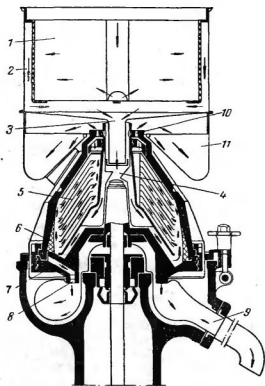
Схематический разрез сепаратора для вина. Фуги — сепаратора для вина.
